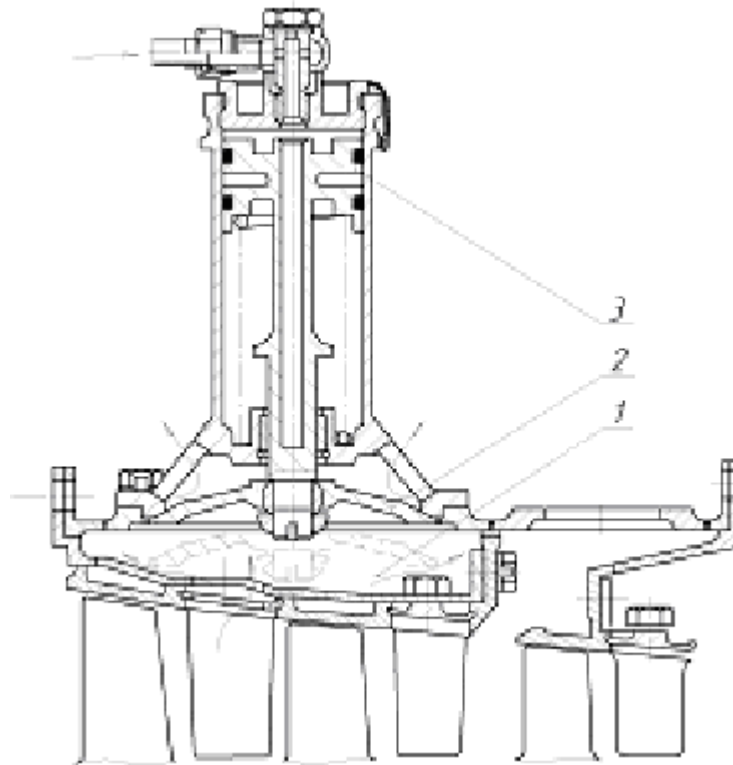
Клапан тарельчатый на компрессоре ПС-90А:
